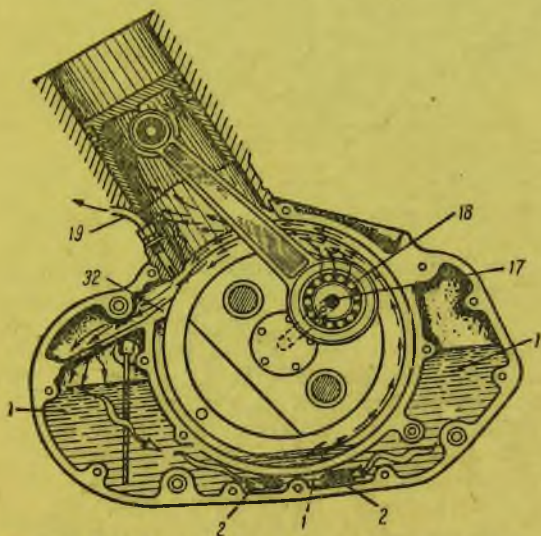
Схема смазки двигателя ТИЗ-АМ-600
